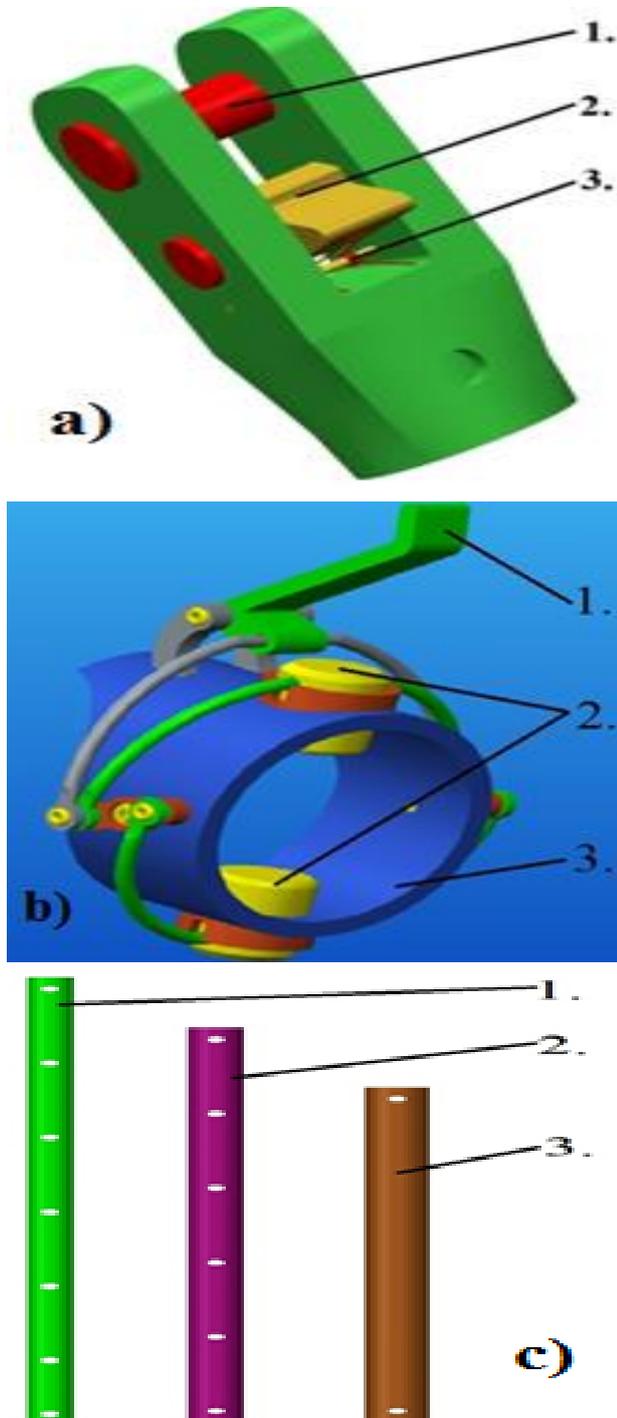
Elementele componente ale subansamblului de susținere: a) cylindrical hinge; b) locking sections system; c) sections;
